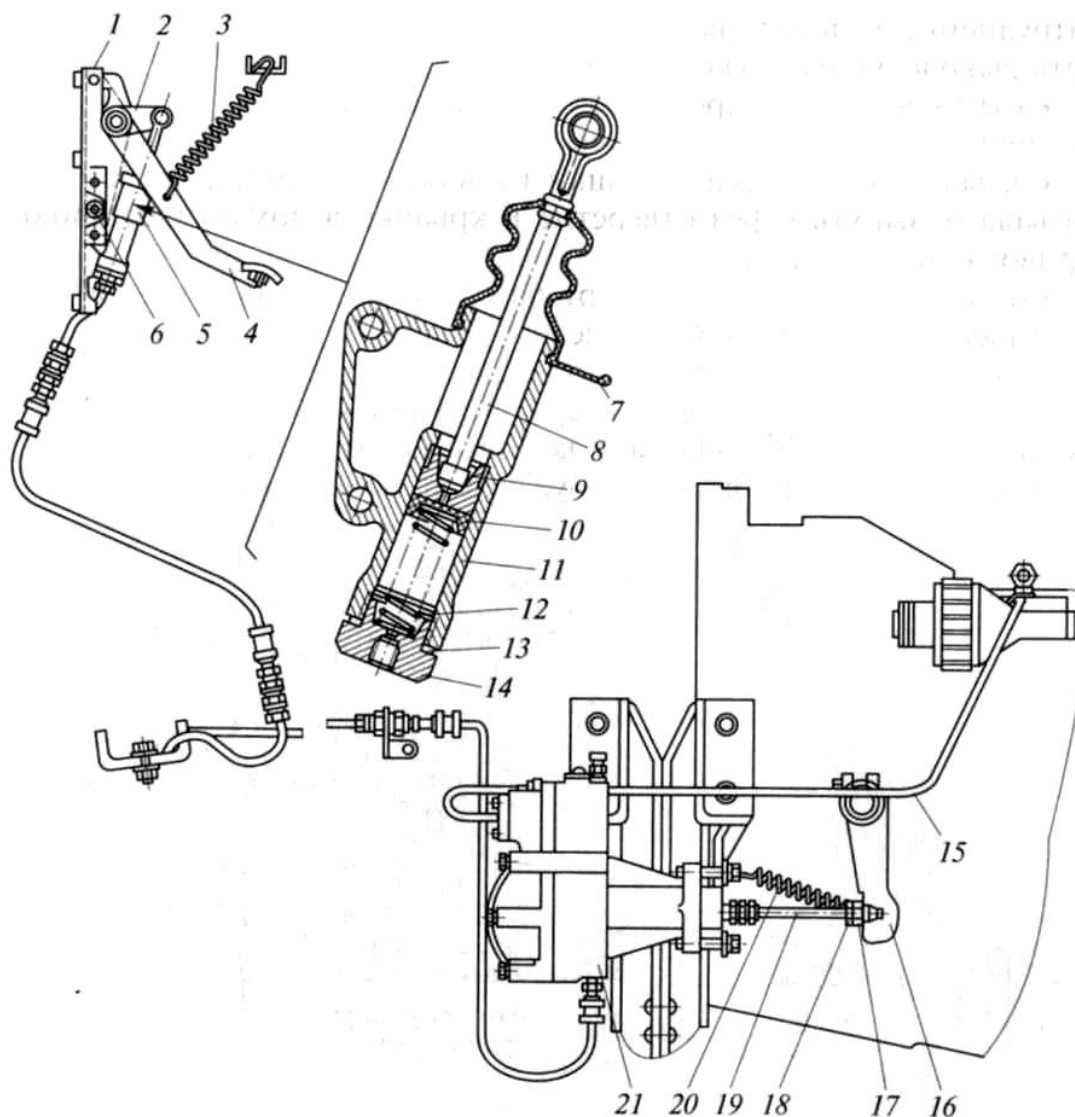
Гидравлический привод сцепления автомобиля КамАЗ-5320:
